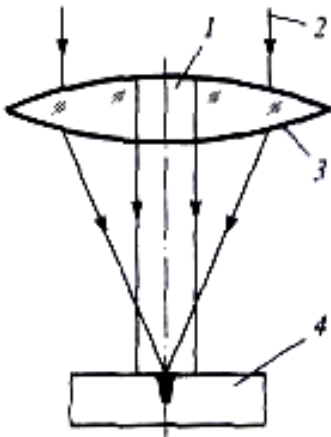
Схема для сварки с подогревом околошовной зоны:
